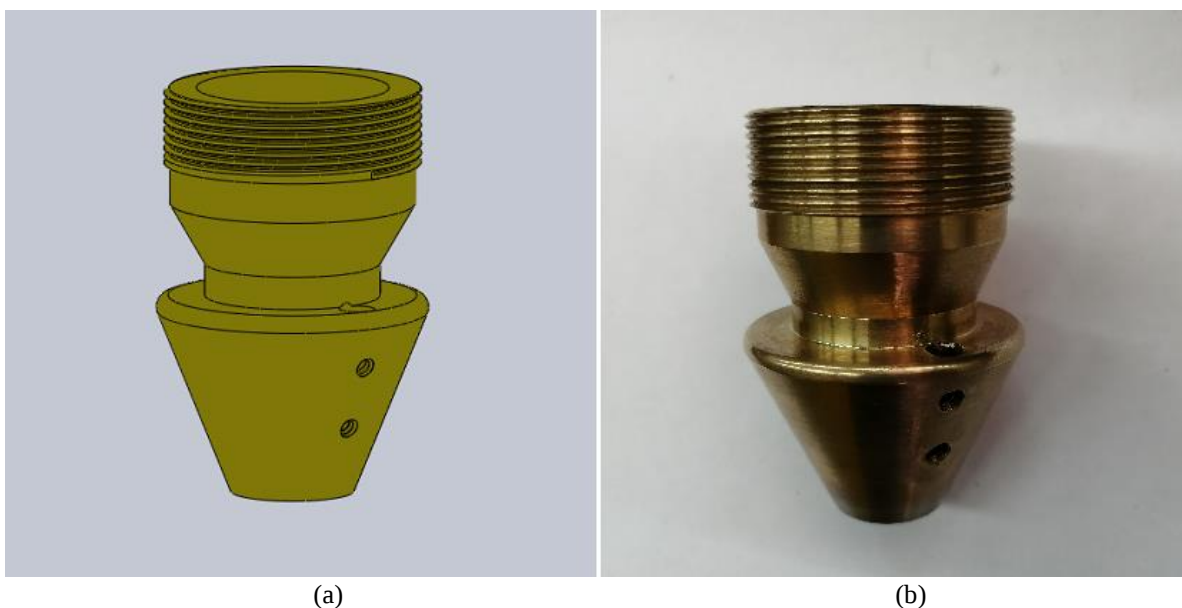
(a) Suporte do bocal projetado. (b) Suporte do bocal fabricado de bronze
